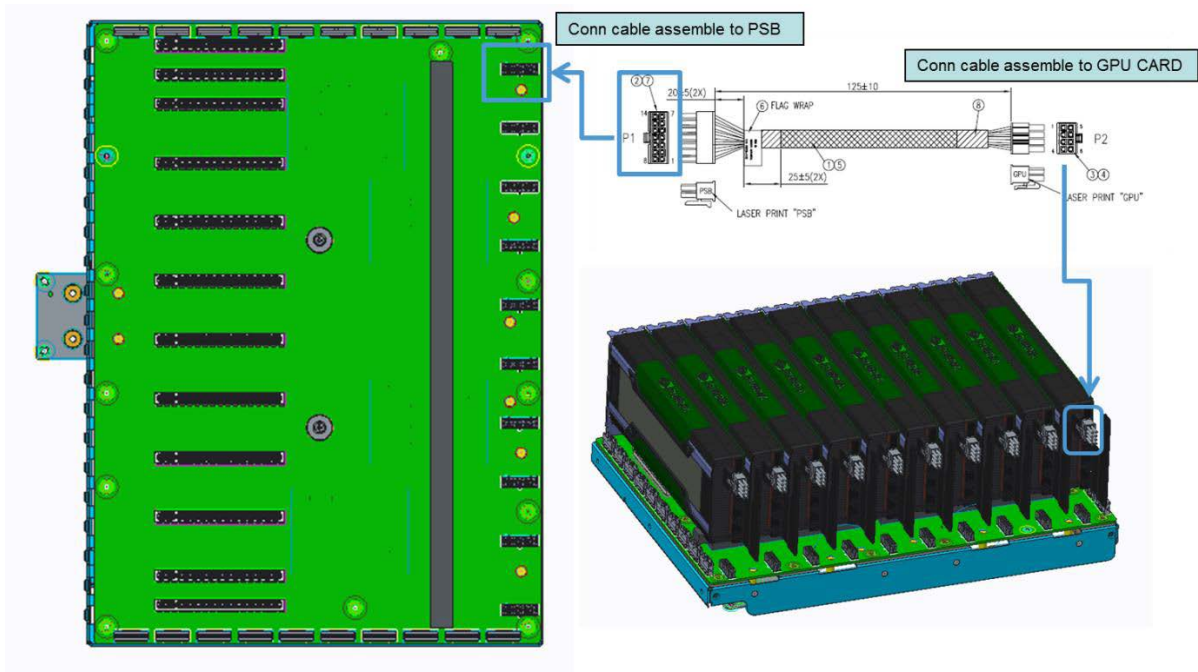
Assemblage du câble d'alimentation GPU, carte GPU vers PSB
